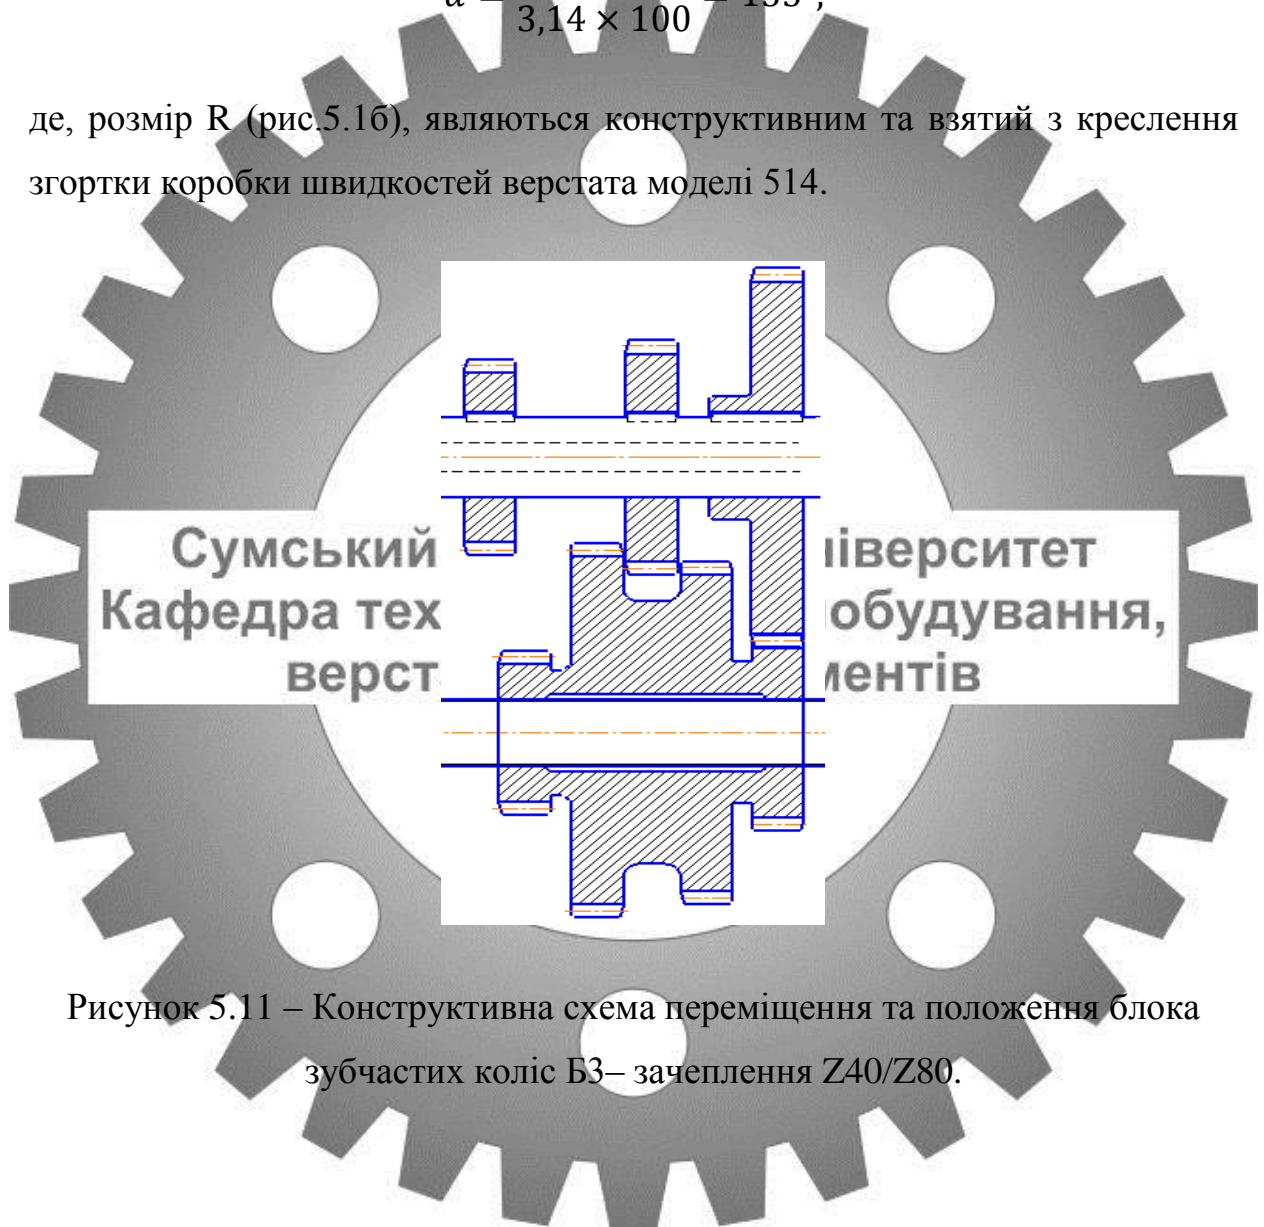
Конструктивна схема переміщення та положення блока зубчатих коліс БЗ– зачеплення Z40/Z80.
